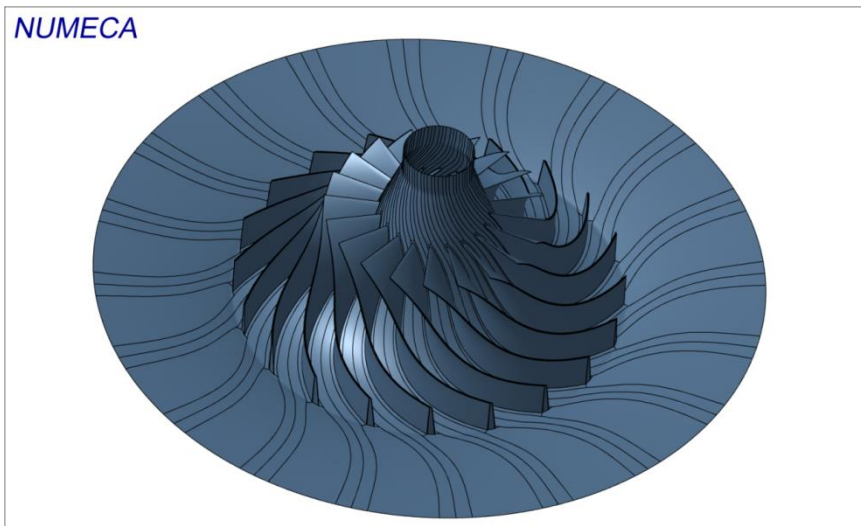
Большой масштабный центробежный компрессор (LSCC)
